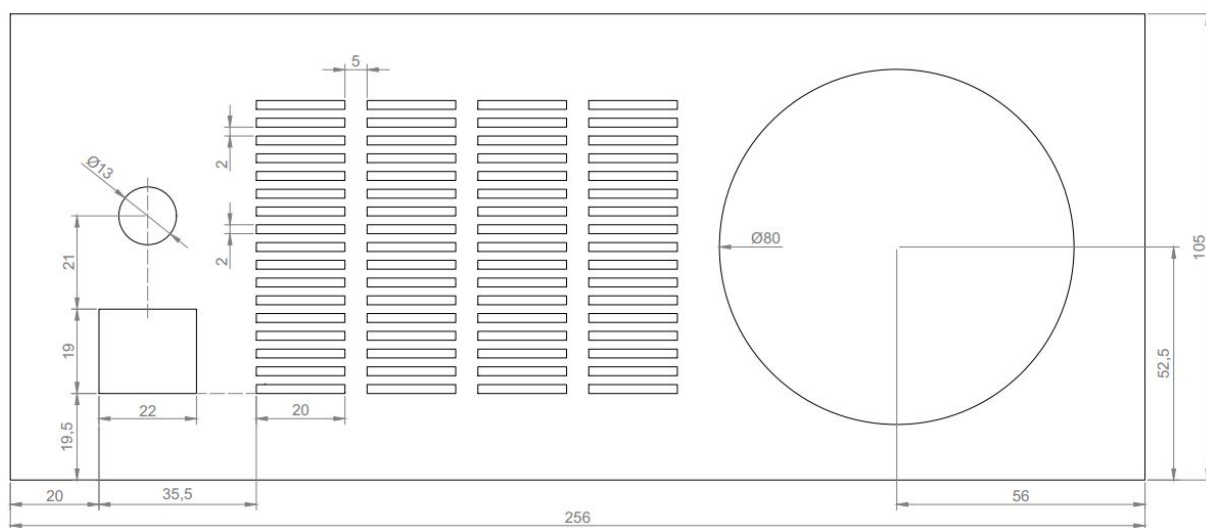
CAD Zeichnung der Gehäuserückseite.
